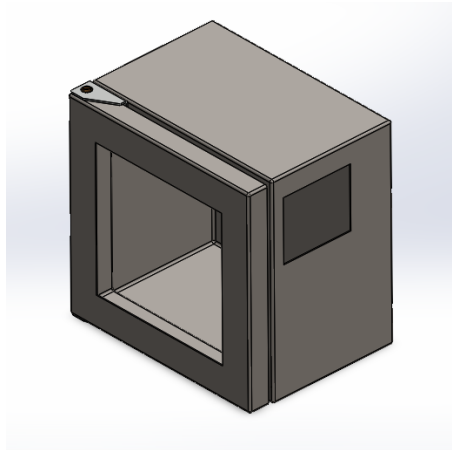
Diseño de estructura de planta en SolidWorks, Elaborado por autores
